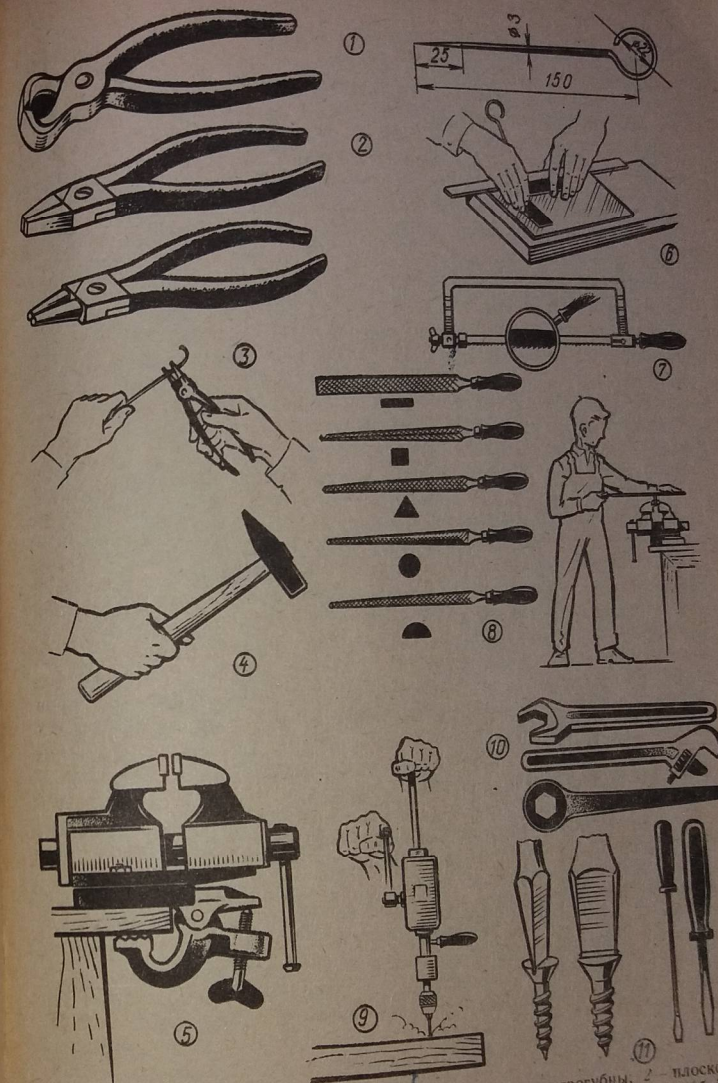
Слесарный инструмент и приспособления: 1 — острогубцы, 2 — плоскогубцы, 3 — круглогубцы и прием работы ими; 4 — молоток с квадратным бойком; 5 — слесарные тиски; 6 — чертилка и прием работы ею; 7 — ножовка; 8 — напильники (плоский, квадратный, трехгранный, круглый и полукруглый) и прием работы напильником; 9 — ручная дрель; 10 — гаечные ключи (открытый, раздвижной, накидной); 11 — отвертки
